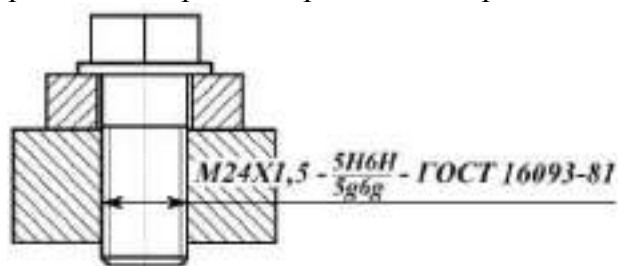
Обозначение резьбового соединения на сборочном чертеже (посадка с зазором)
